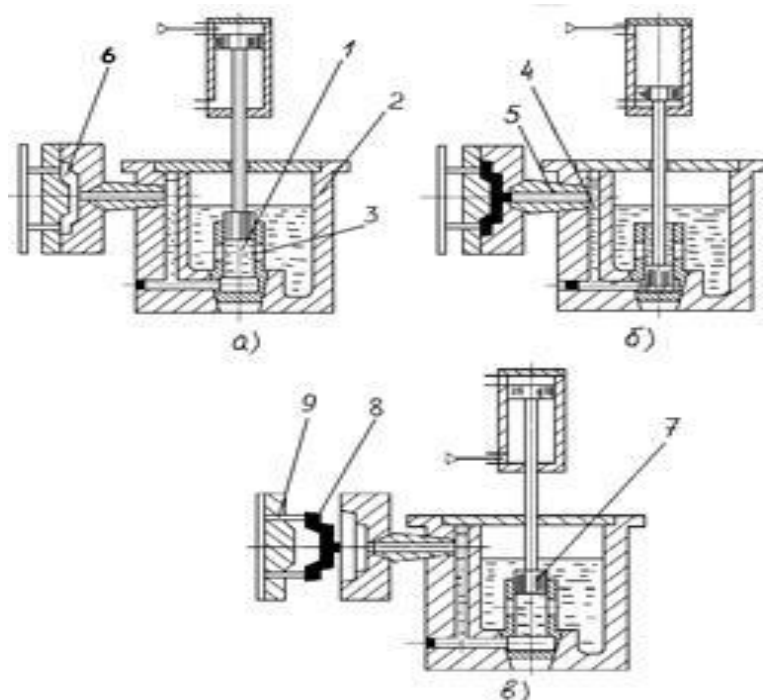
Машина ЛПД с горячей камерой прессования
